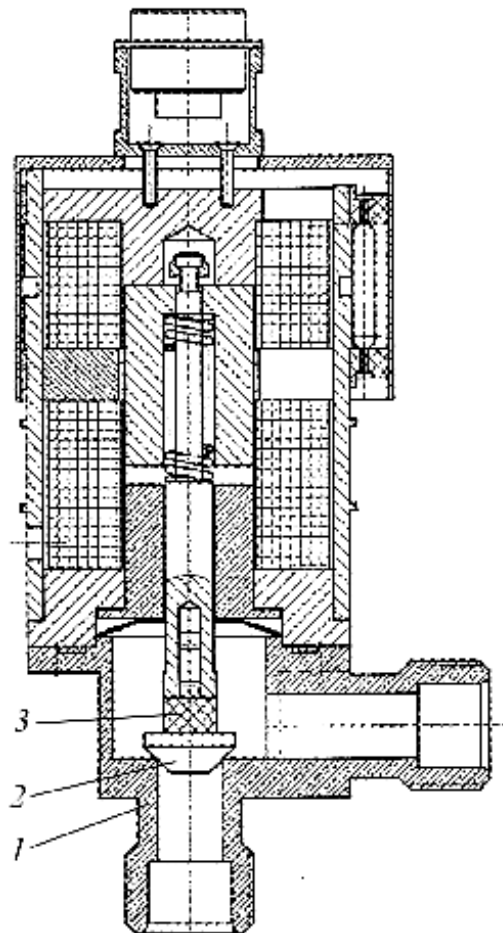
Конструктивна схема експериментального зразка клапана з жорстким ущільненням запірного вузла типу “метал–метал”: 1 — сталевий затвор; 2 — сталевий корпус з сідлом; 3 — демпфівувальний елемент
